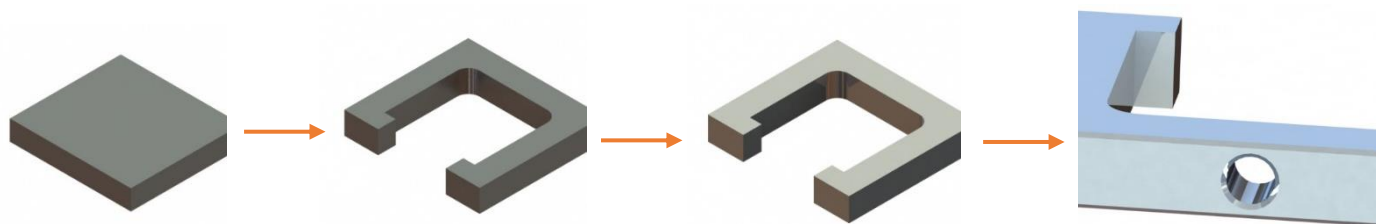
Proceso de manufactura de Prensa del Bloque “V”
